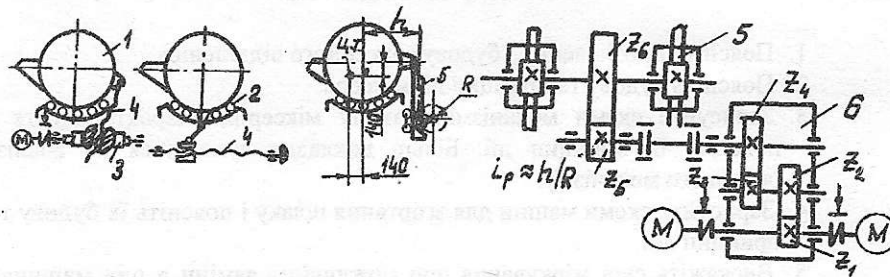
Схеми механізмів повороту міксерів: 1-міксер; 2-роликів обійма; 3-спеціальний черв'ячний редуктор; 4-гвинтова передача; 6-привод; 5-рейка
